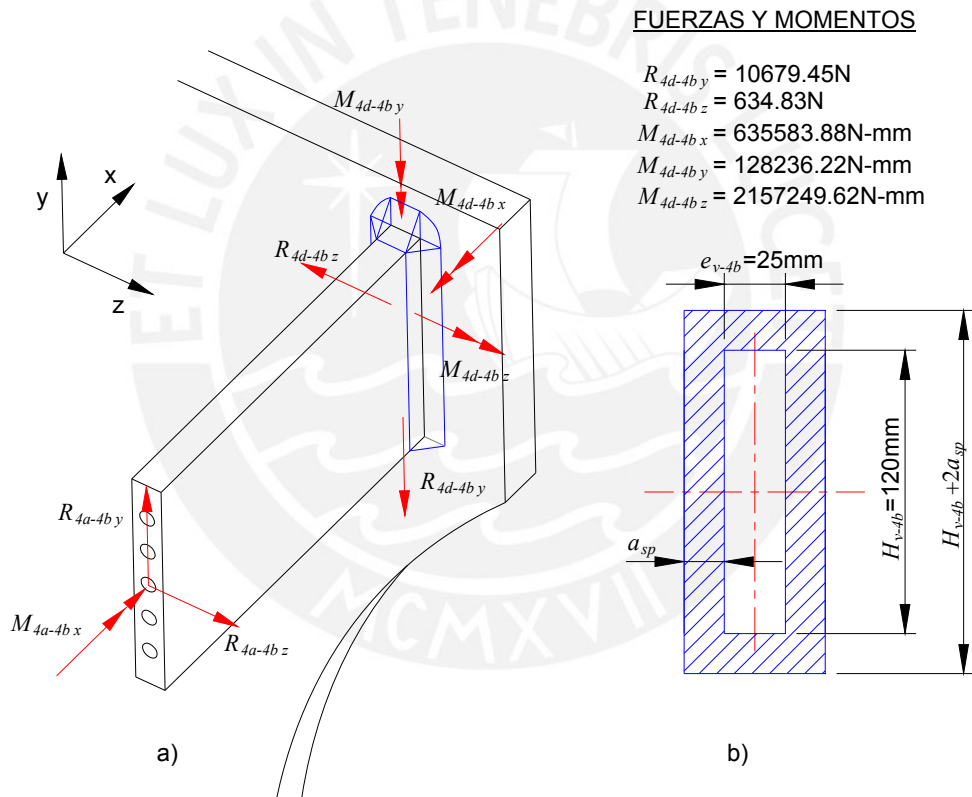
Esquemas de las soldaduras del voladizo a) Fuerzas actuantes b) Sección transversal de la unión soldada [Elaboración propia]
